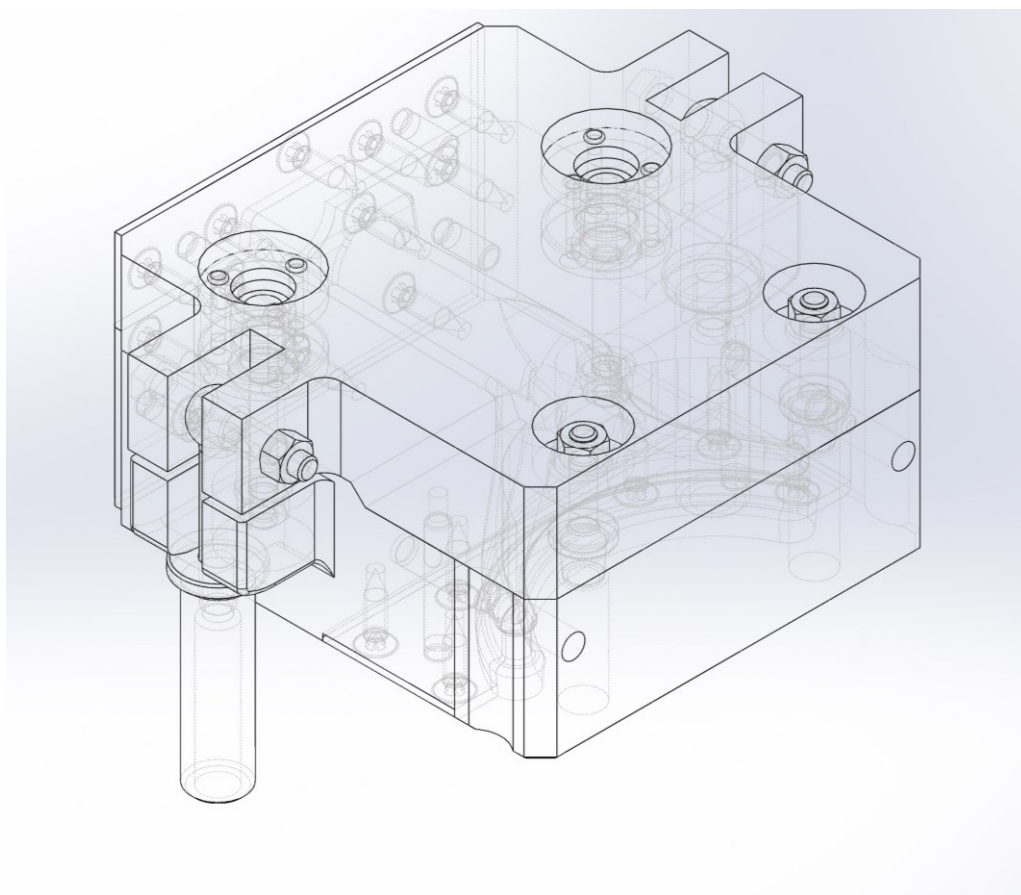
3Д зборка компоновки стержня та заготовки (основи)
